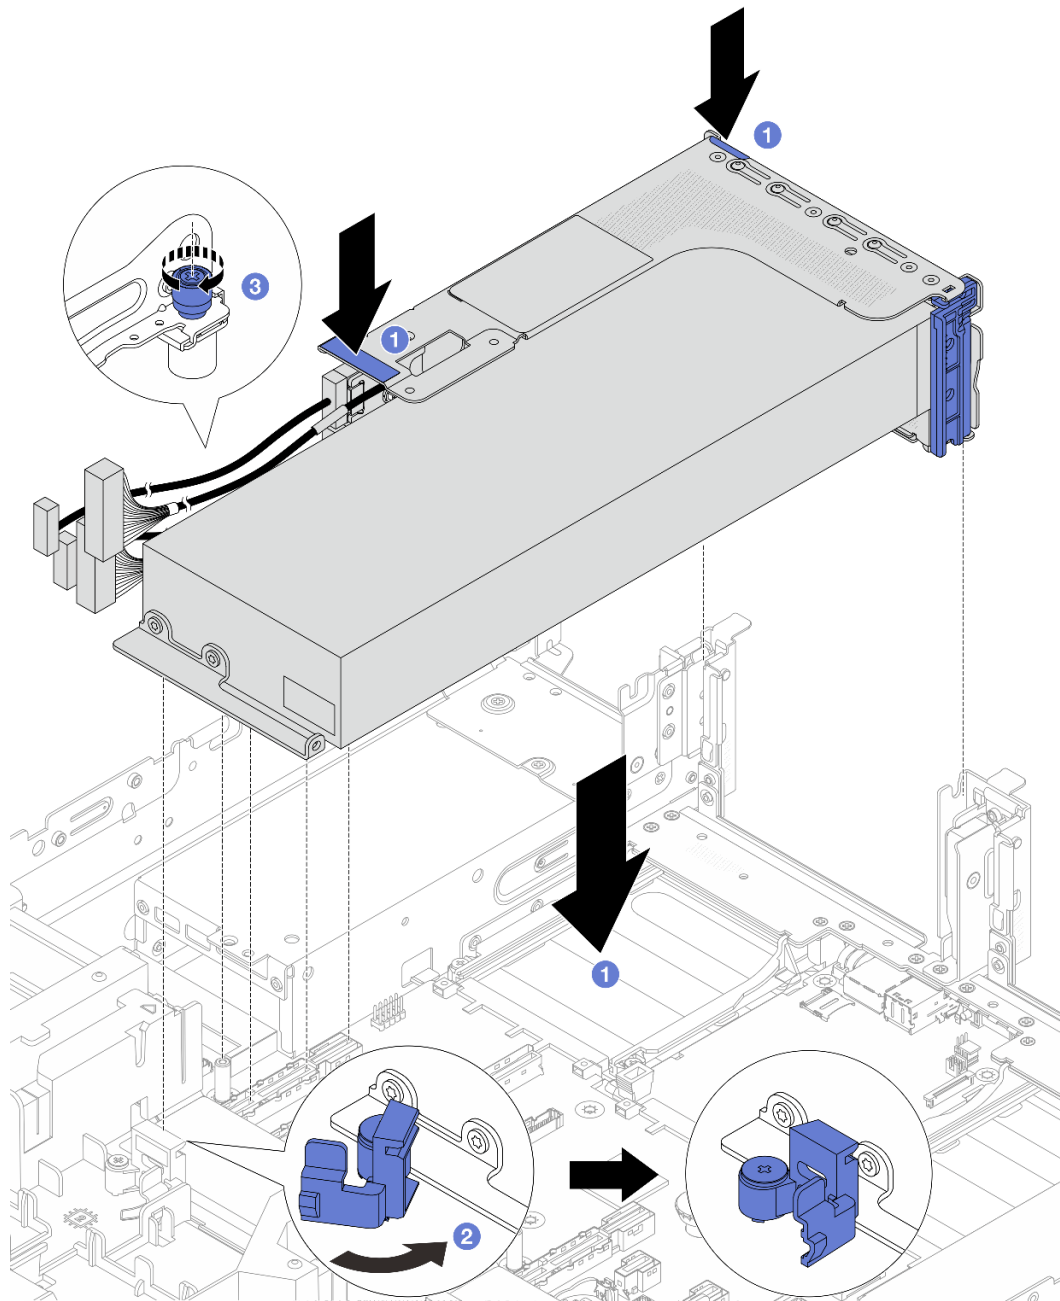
Installieren der Adapterkartenbaugruppe mit GPU-Adapter
